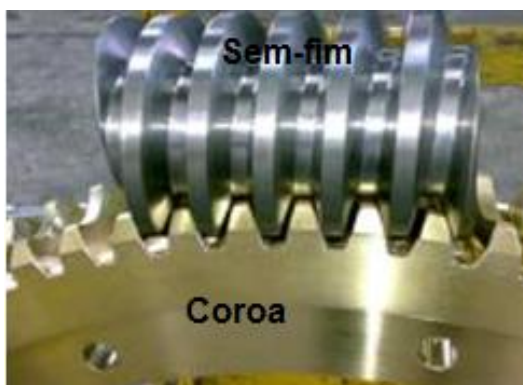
Parafuso sem-fim e engrenagem helicoidal.
